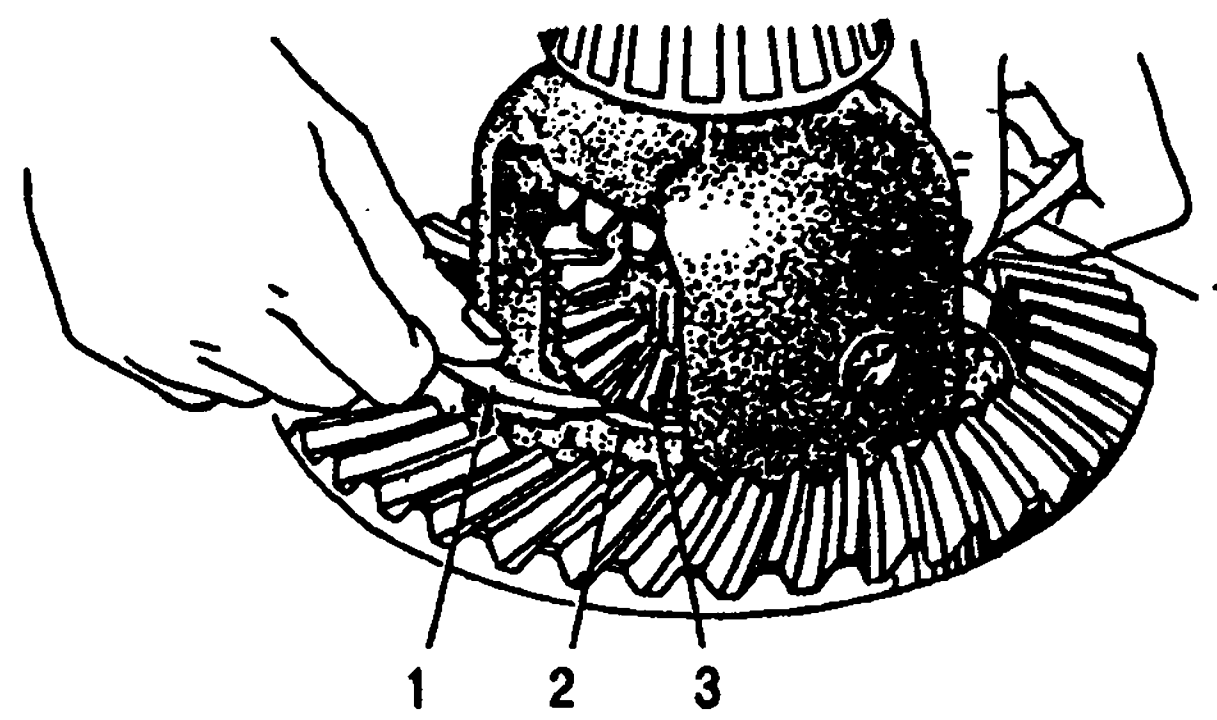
Проверка зазора полуосевых шестерен в дифференциале: 1 - щуп; 2 - упорная шайба; 3 - полуосевая шестерня
